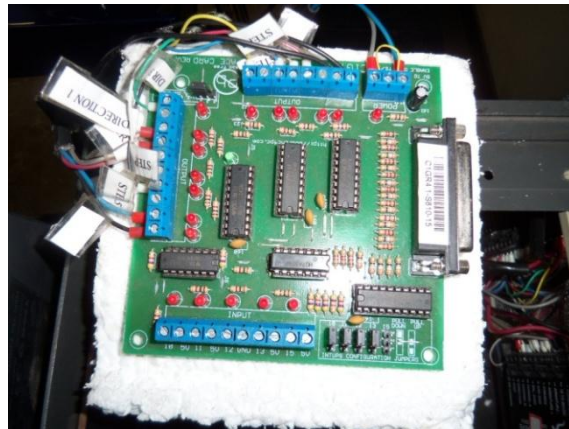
Arranjo de ligação da placa modelo C1G - Breakout Board.
